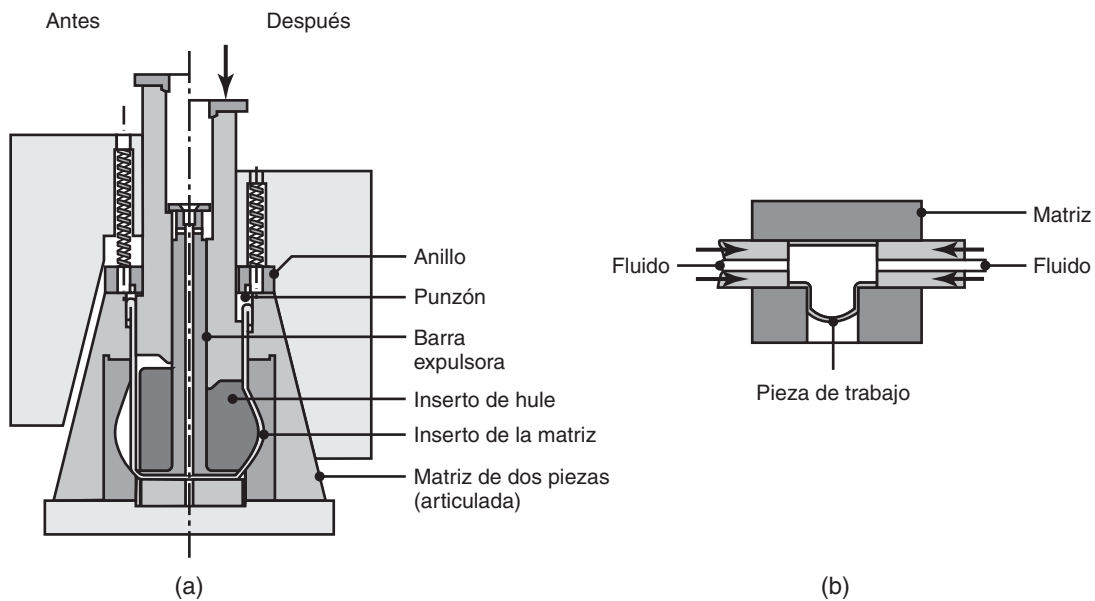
(a) Abombado de una parte tubular con un inserto flexible. Las jarras para agua se pueden fabricar mediante este método. (b) Producción de accesorios para plomería mediante la expansión de piezas tubulares sometidas a presión interna. Después se punzona hacia fuera el fondo de la pieza para producir una "T". Fuente: J. A. Schey.
